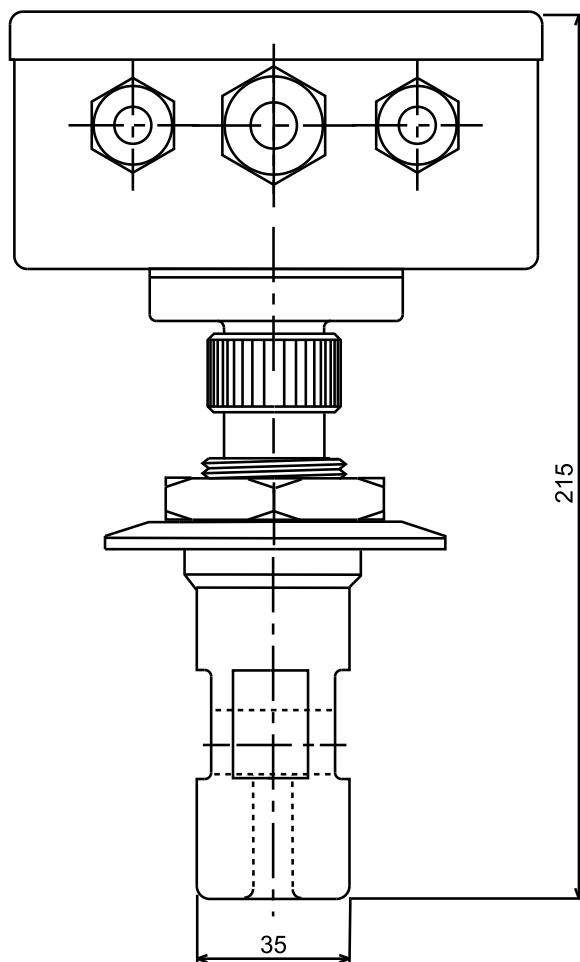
Габаритные размеры датчика IET40L с хомутным присоединением (вид спереди)
